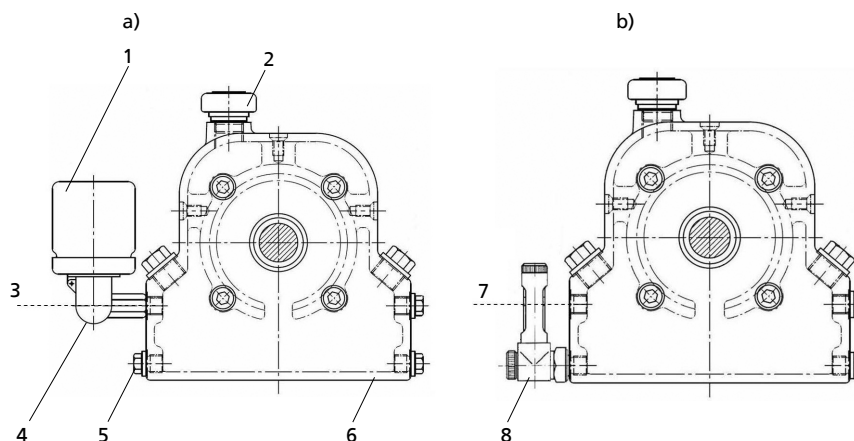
а) Корпус подшипников с регулятором уровня масла - б) Корпус подшипников с указателем уровня масла
